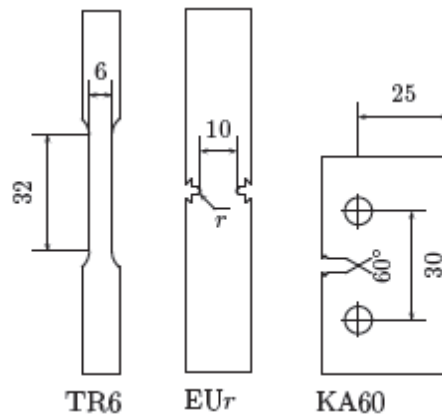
Géométrie des éprouvettes : traction lisse (TR6), entaillée en U (EUR), éprouvette Kahn (KA60) [66]
